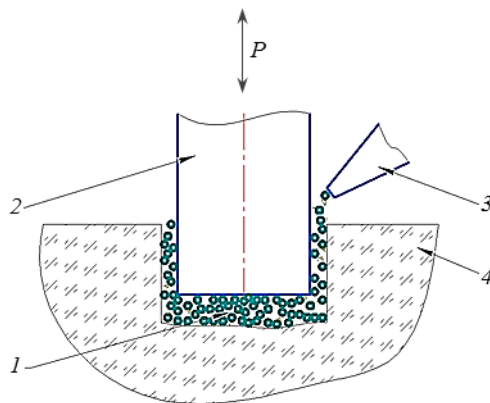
Принцип размерной ультразвуковой обработки: 1 – суспензия абразивного порошка; 2 – режущий инструмент; 3 – подача суспензии; 4 – обрабатываемый материал (изделие)
